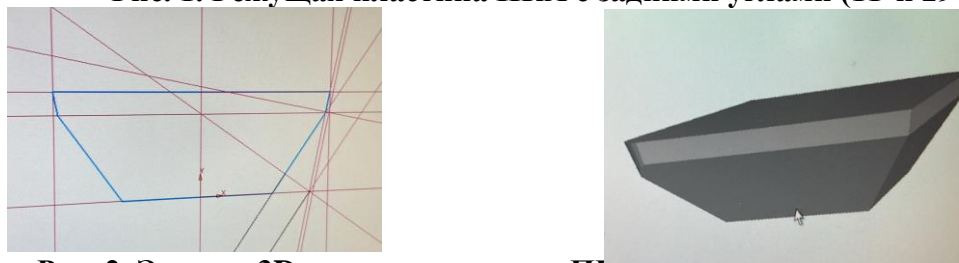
Эскиз и 3D-модель пластины ПКА с задними углами (11° и 29°)
